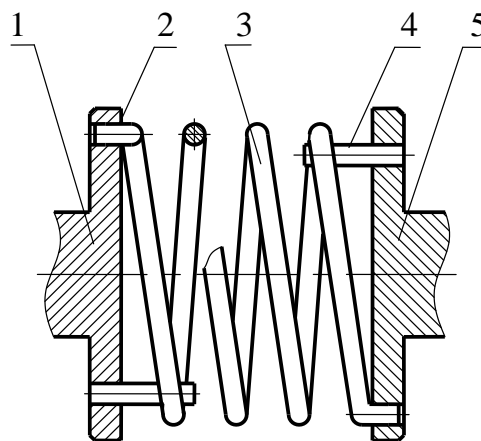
Гнучкий вал із циліндричною пружиною:
